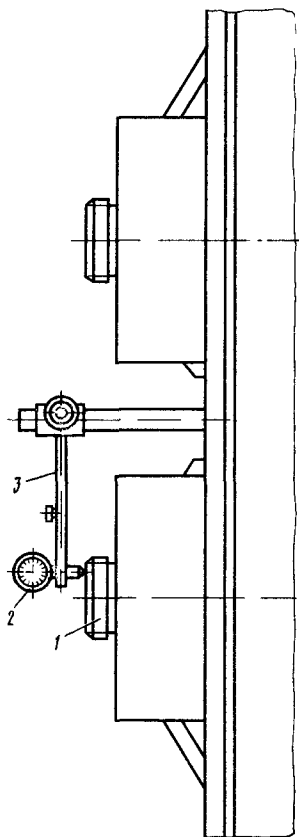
Проверка осевого разбега рабочих колес воздуходувки дизеля 2Д100.
